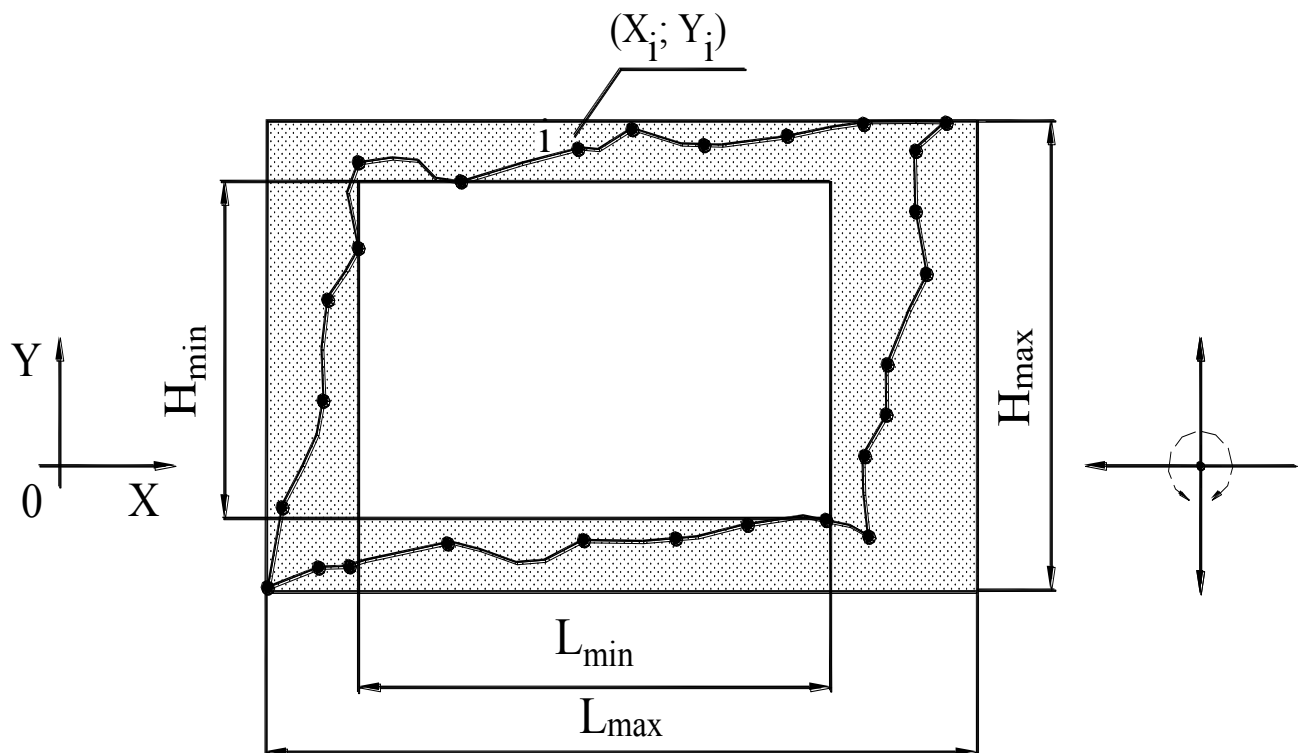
Контроль размеров детали на основе принципа перераспределения полей допусков
